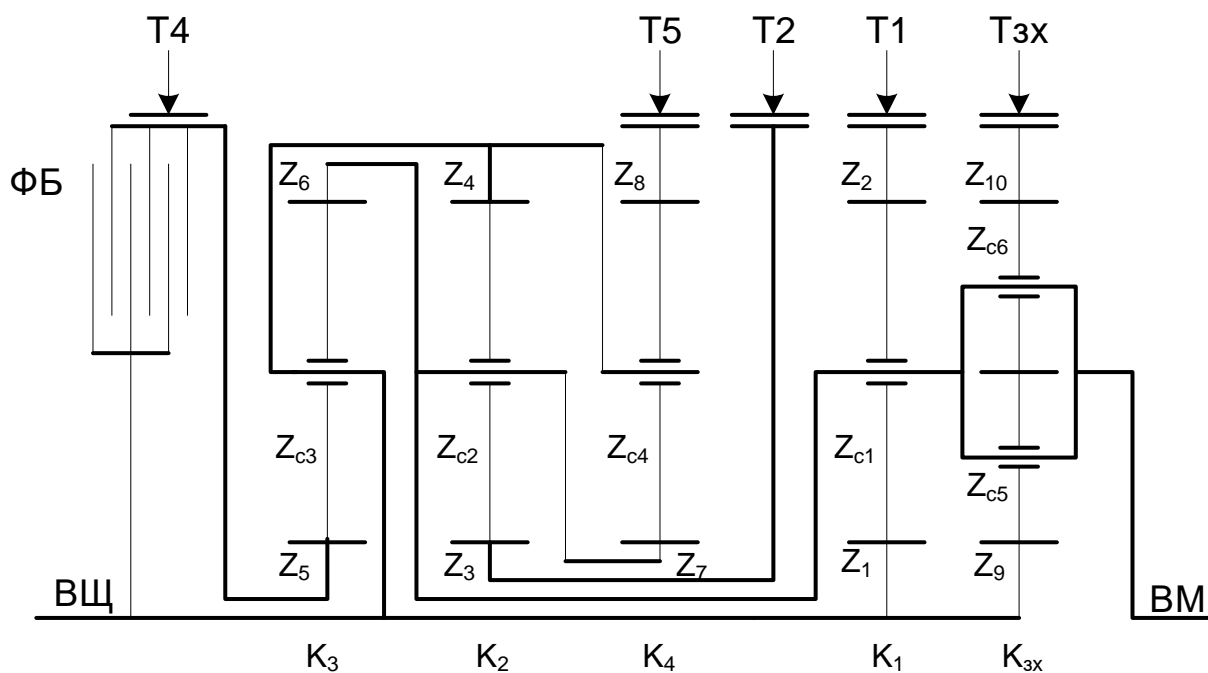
Кинематическая схема планетарной коробки передач типа 5+1 с двумя повышающими ступенями
